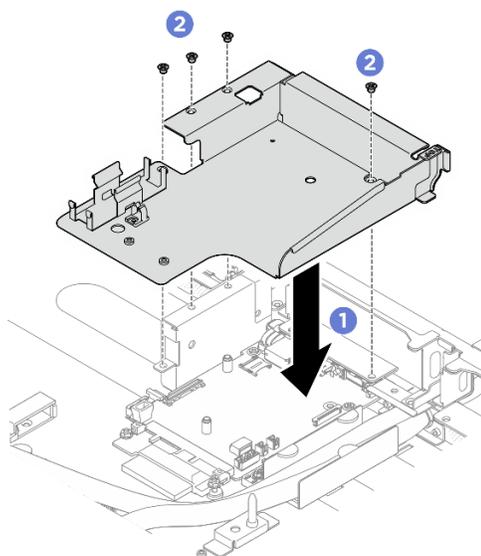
Instalando o suporte do portador do módulo do sensor de vazamento
